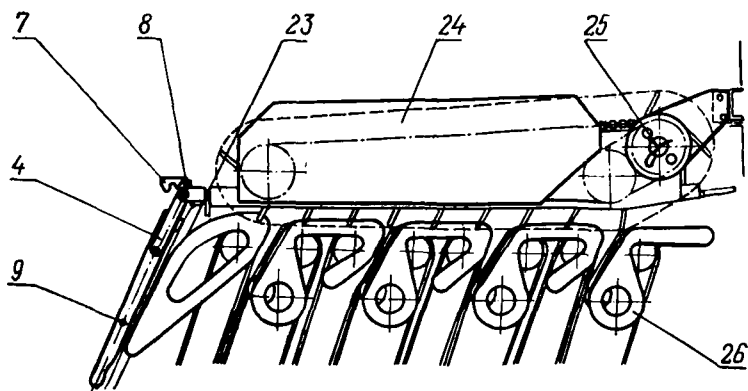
Переоборудованный поперечный транспортер в рабочем положении:
